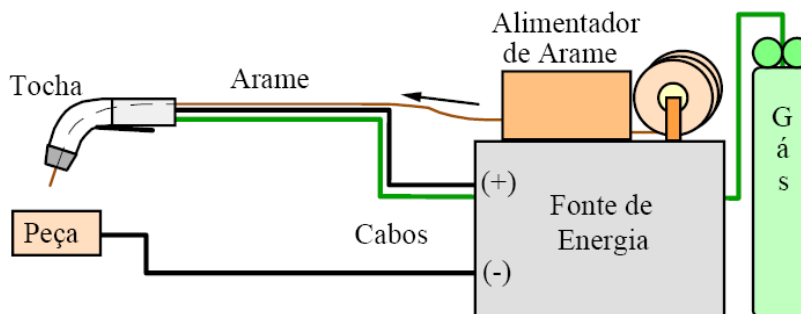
Esquema do equipamento de soldagem MIG.
